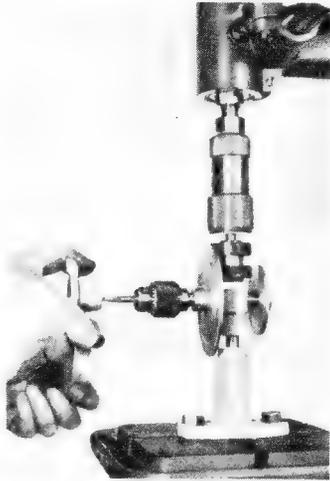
Gewindeschneid-Halbotomat, an einer Bohrmaschine angebracht
